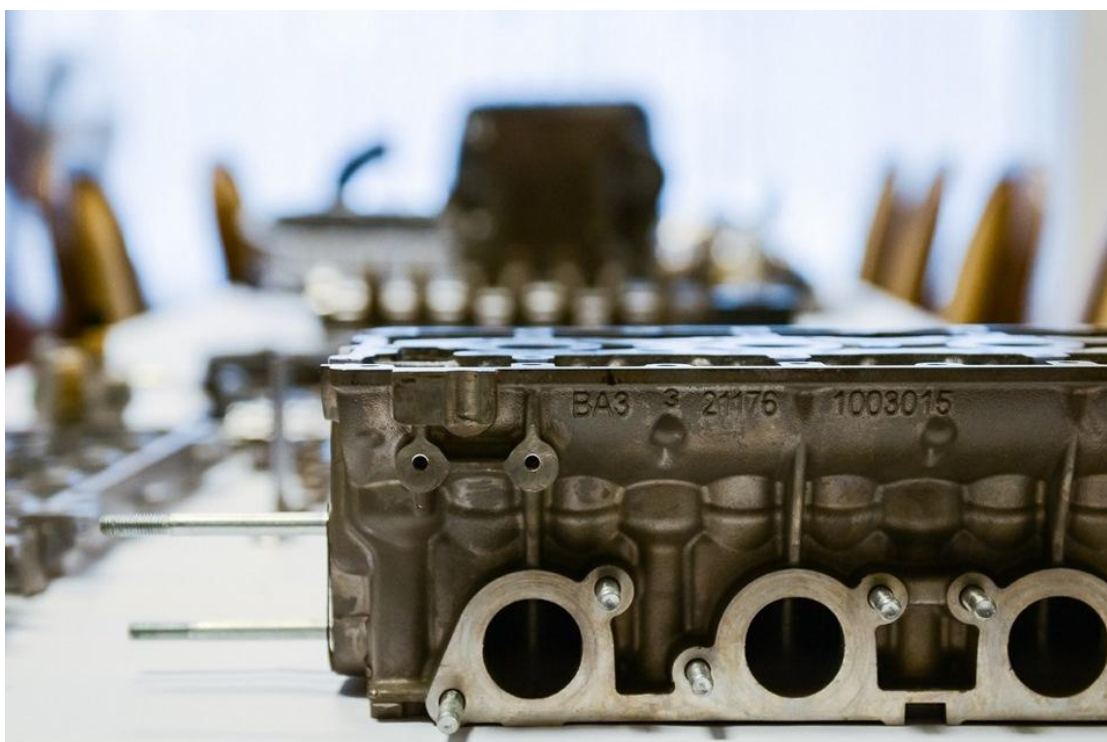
Блок цилиндров двигателя 21179 (вид сбоку)
